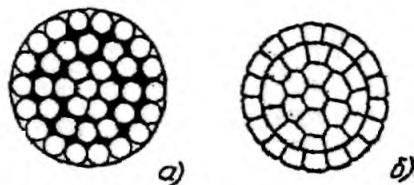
Схема круглой токопроводящей жилы: а - неуплотненной, б - уплотненной
